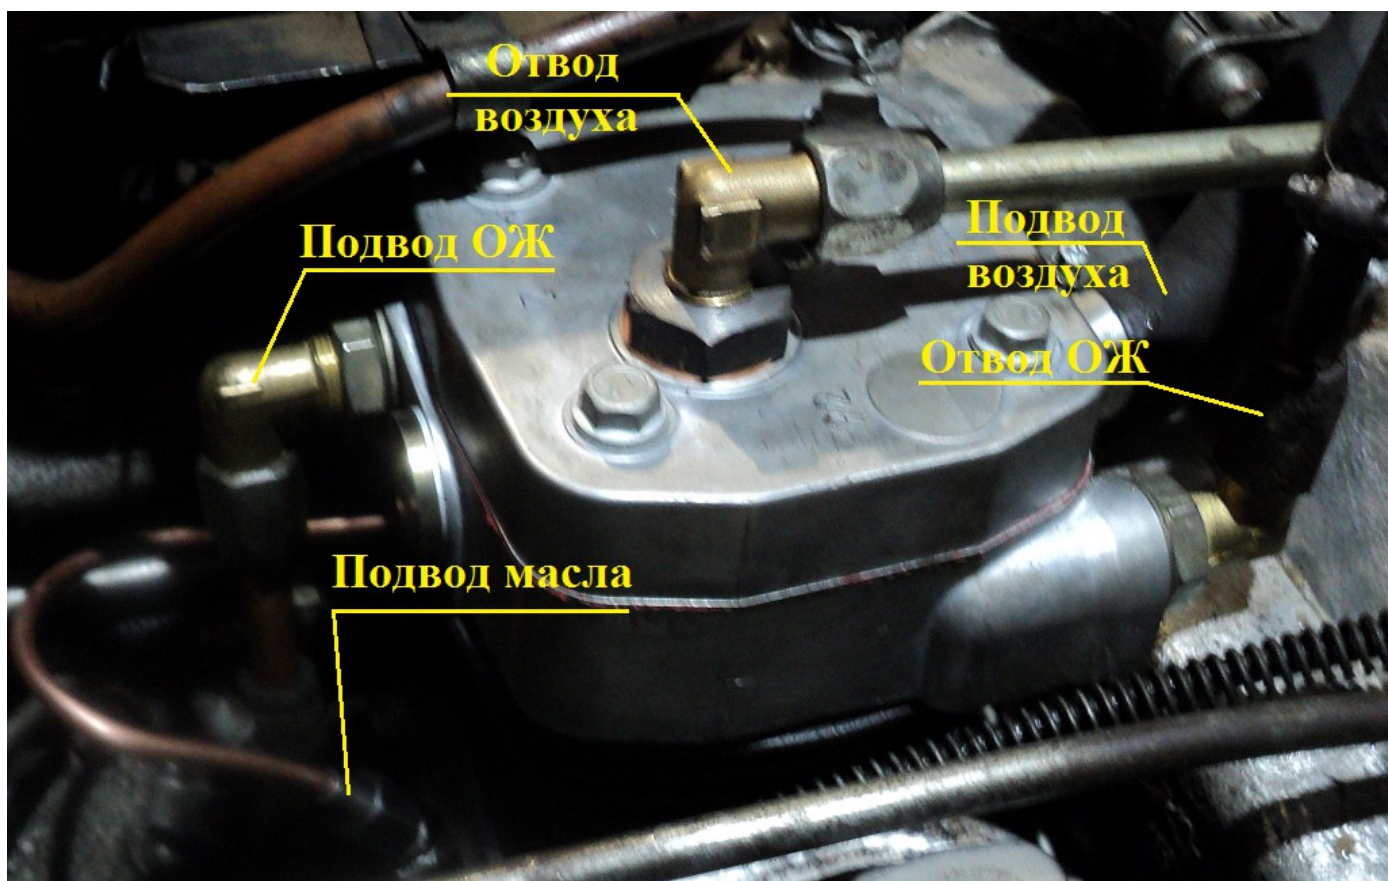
Монтаж отвода ОЖ и воздуха из компрессора и подвода воздуха к компрессору
